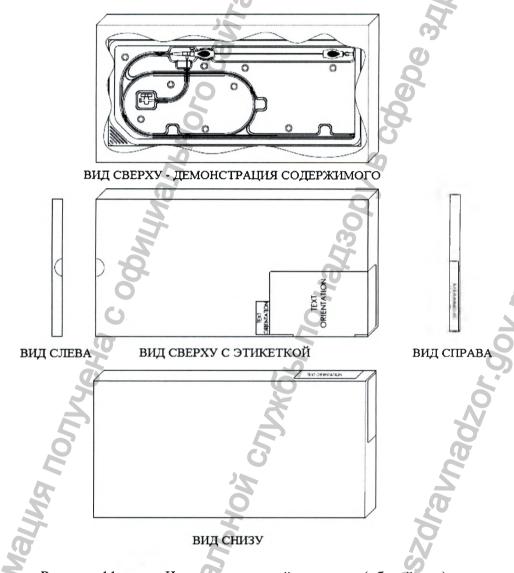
Чертеж вторичной упаковки (общий вид)
